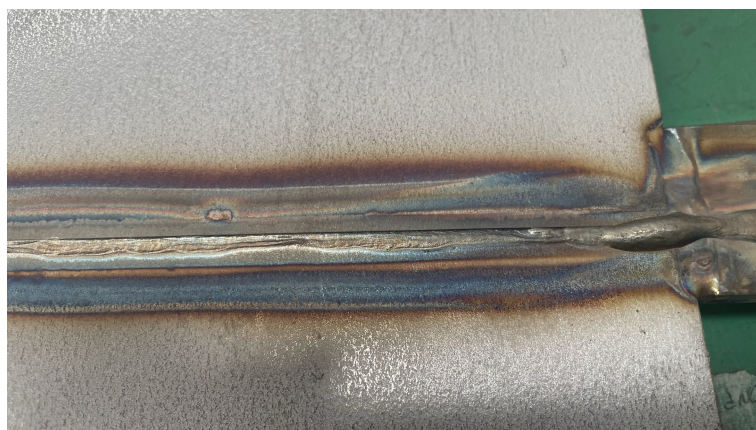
Provete inválido - falta de penetração de soldadura.
